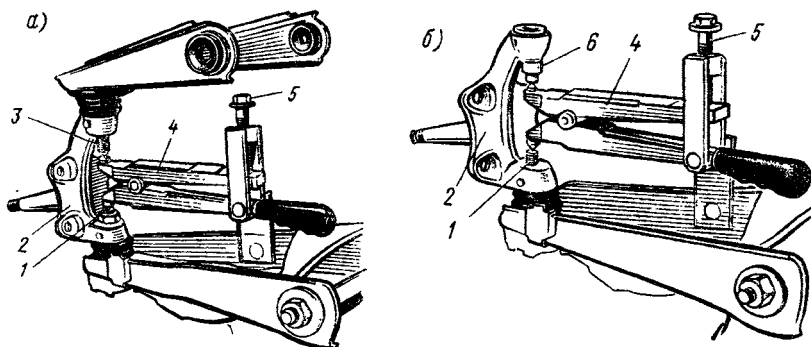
Выпрессовка пальцев шаровых шарниров передней подвески:
